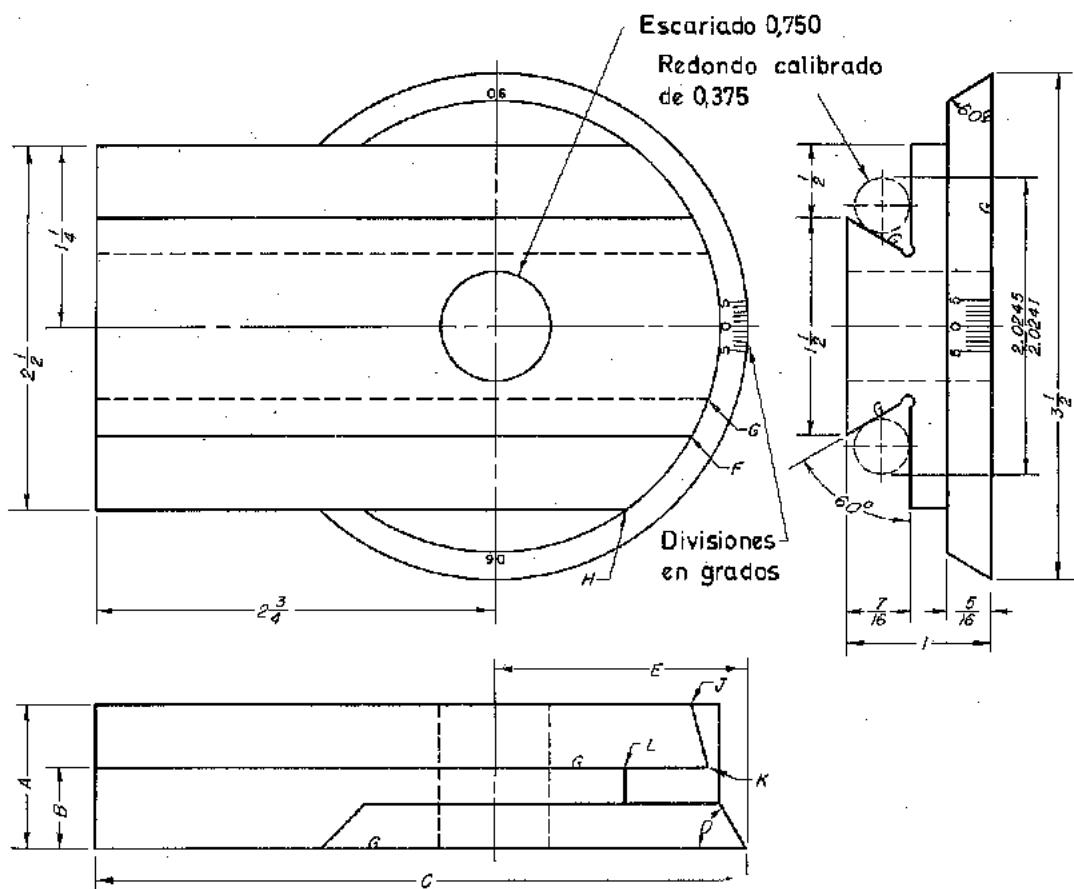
Guía inferior con apoyo en la cola de milano (Cotas en pulgadas).
